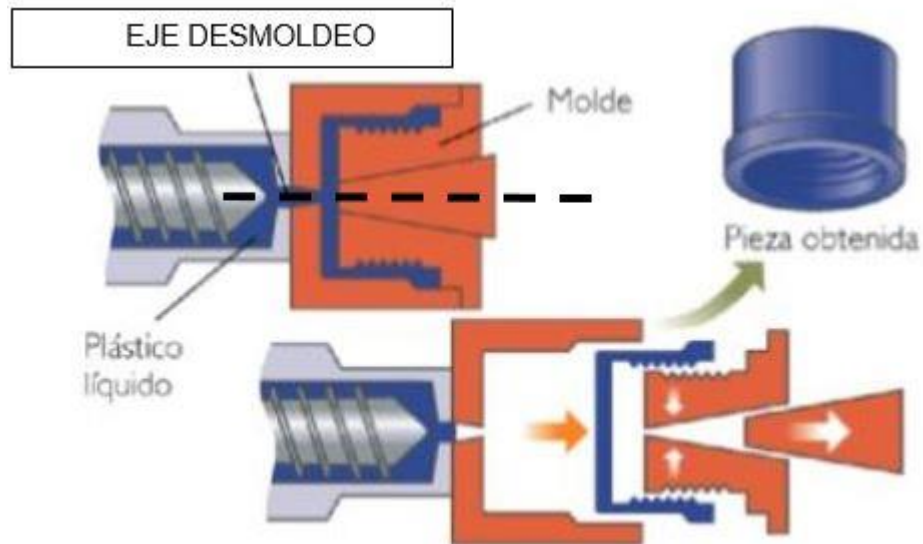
Eje de desmoldeo para proceso de fabricación. [30]
